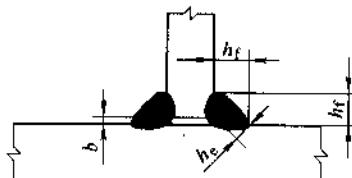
直角角焊缝及搭接角焊缝计算厚度示意
